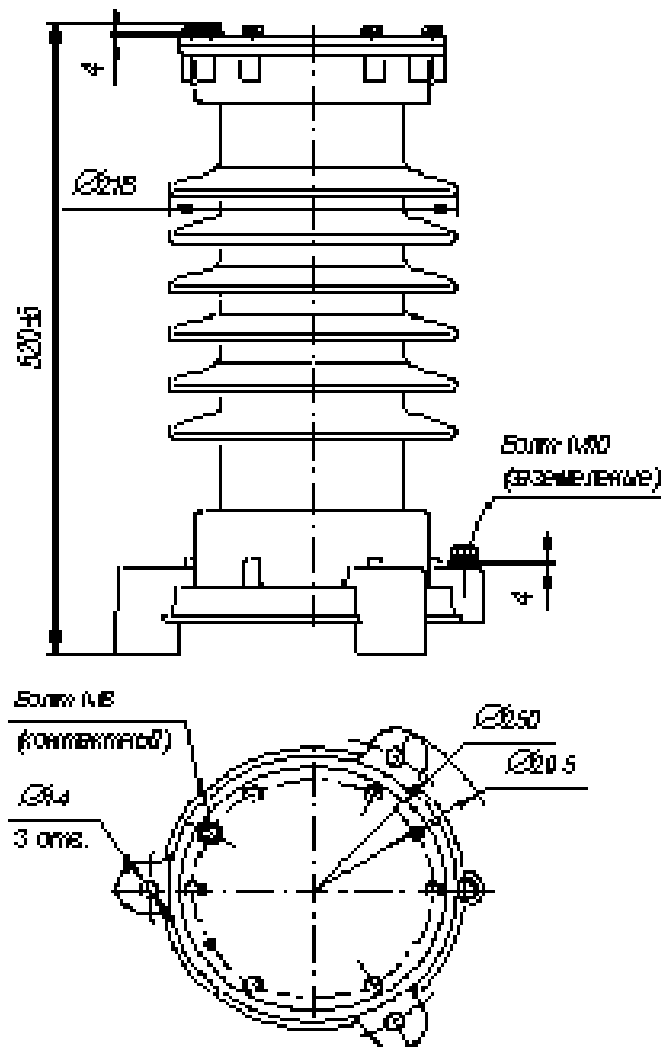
Вид загальний кА конструкція обмежувача перенапруг марки ОПН – 35УХЛ1
